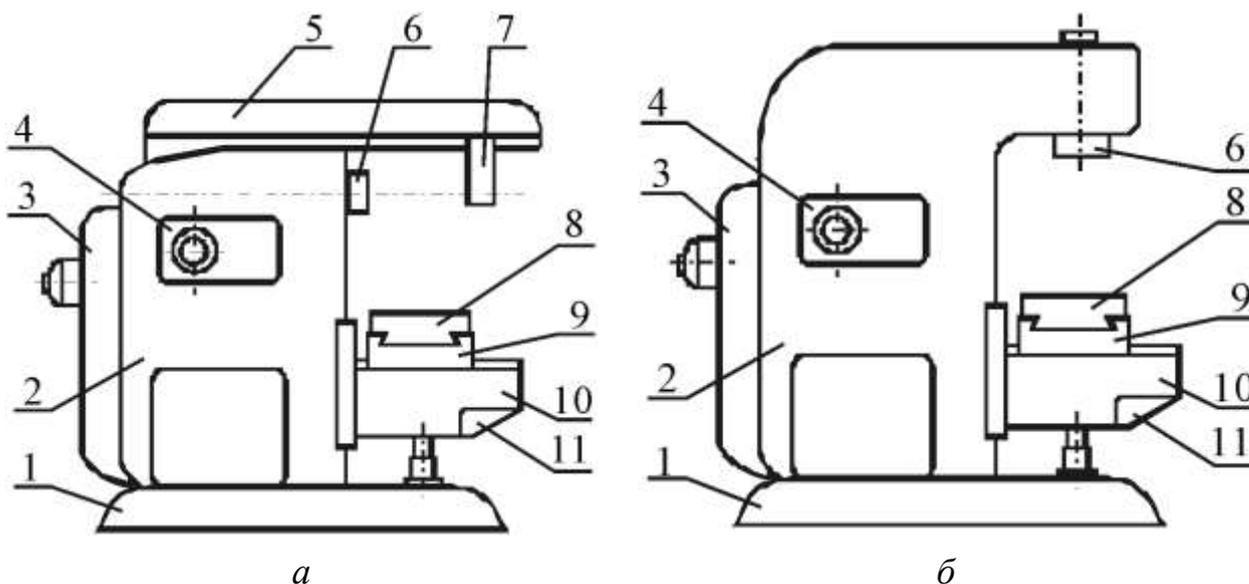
Горизонтально-фрезерний (а) та вертикально-фрезерний (б) верстати
